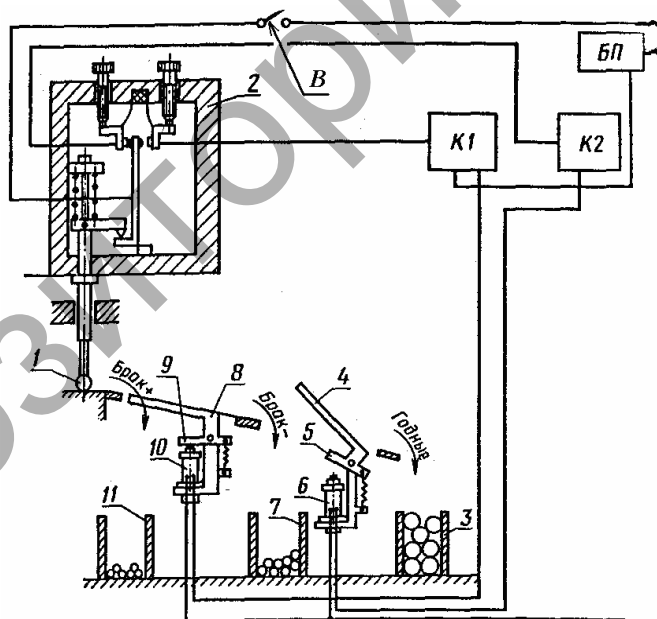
Схема контрольного автомата для сортировки деталей по размеру на три группы
